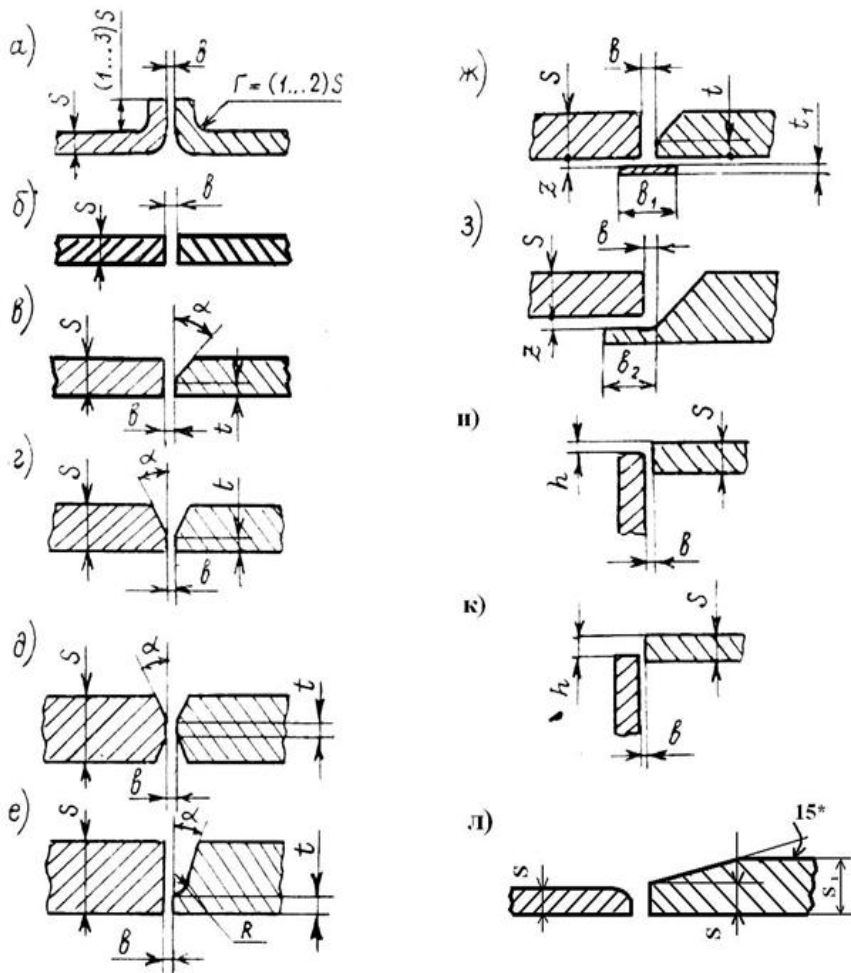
Виды подготовки кромок под сварку: а - с отбортовкой кромок; б, и, к - без скоса кромок; в - со скосом одной кромки; г - со скосом двух кромок; д - с двухсторонним скосом двух кромок; е - с криволинейным скосом кромок; ж - с использованием остающейся или съемной подкладки; з - с замковым расположением деталей; л - дополнительным скосом для устранения влияния разной толщины
